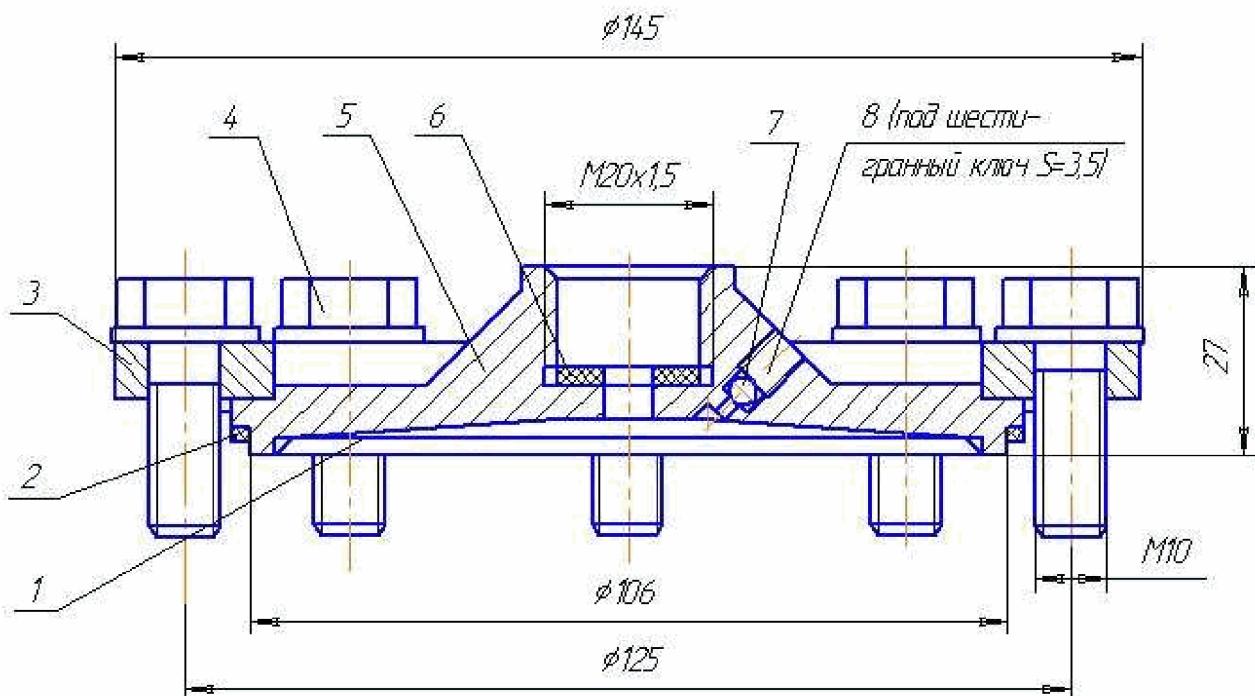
Конструкция, габаритные и присоединительные размеры
